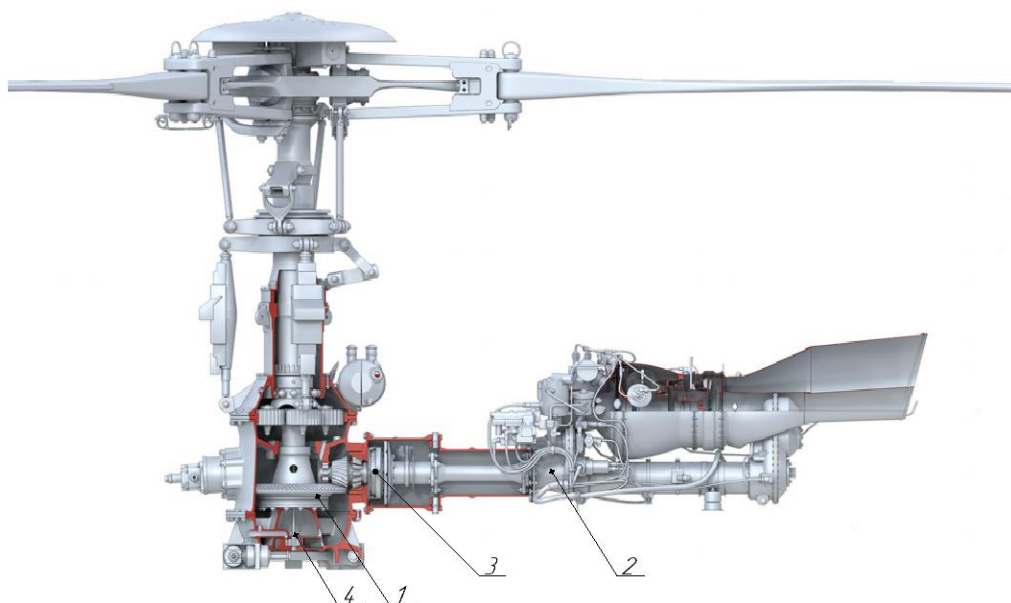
Общий вид трансмиссии: 1 – главный редуктор; 2 – редукторы двигателей; 3 – муфты включения сцепления и свободного хода; 4 – опоры валов с амортизаторами.
